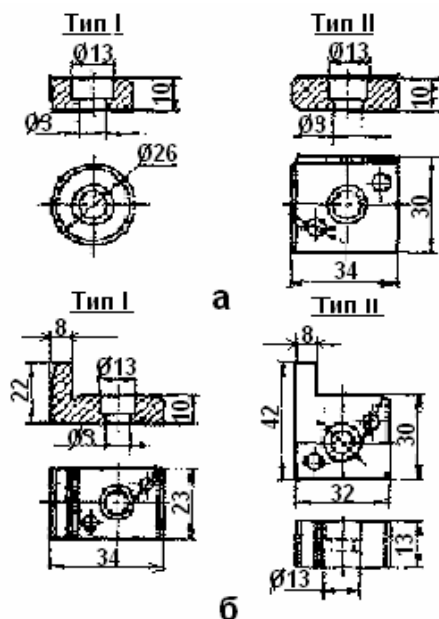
Висотні установки для фрез: а – висотний; б – кутовий
